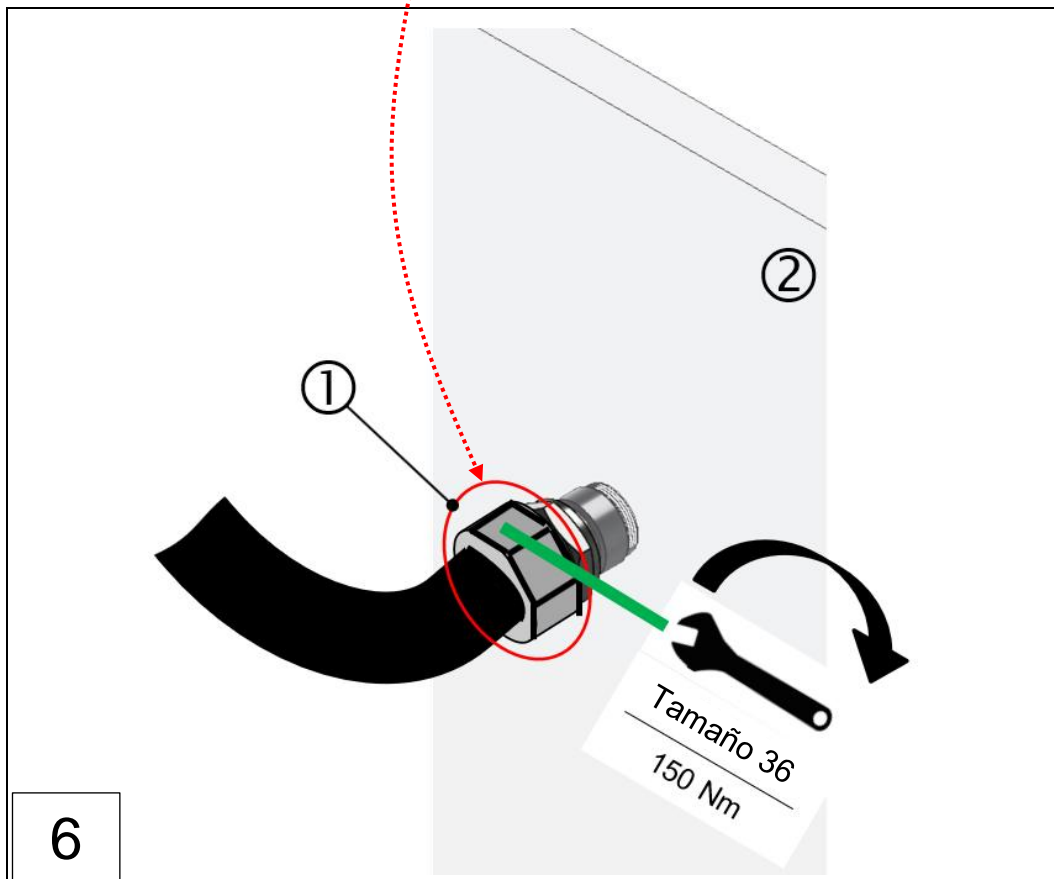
Montaje del tubo de retorno, KIT de actualización VN2020 (pasos 1-6)
